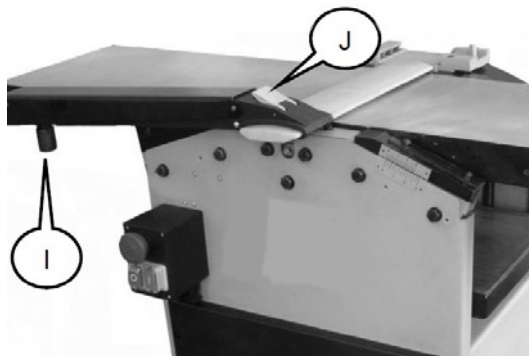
Réglage du couvercle de l'arbre de coupe
